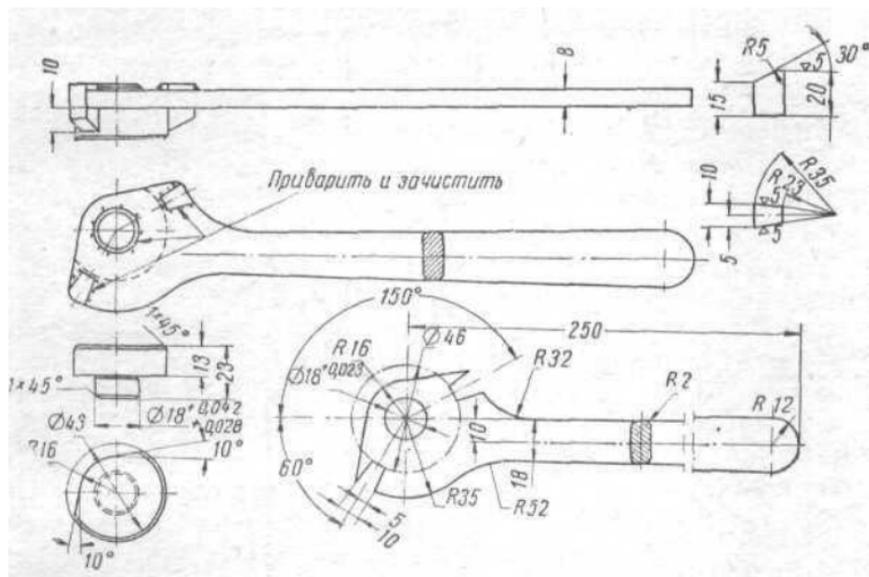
Ключ для регулировочных гаек подшипников коробки дифференциала
